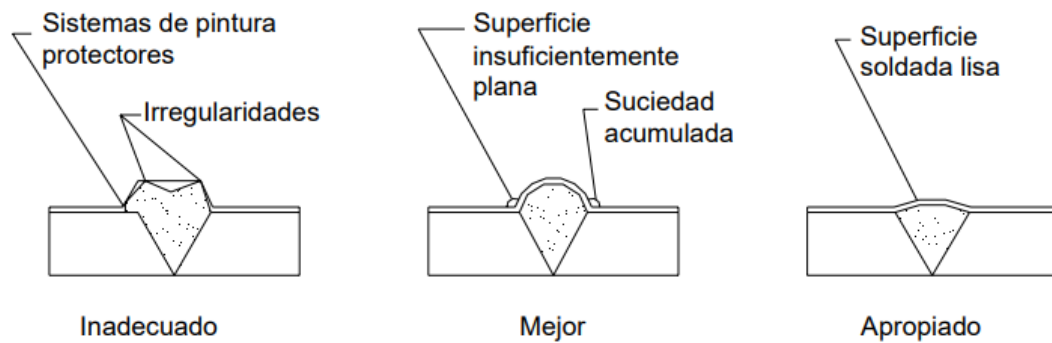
Comparativa de perfiles de soldadura. 2025. Fuente: Urbán Brotóns, P. (2010). Construcción de estructuras metálicas. 4.ª ed. ECU.
